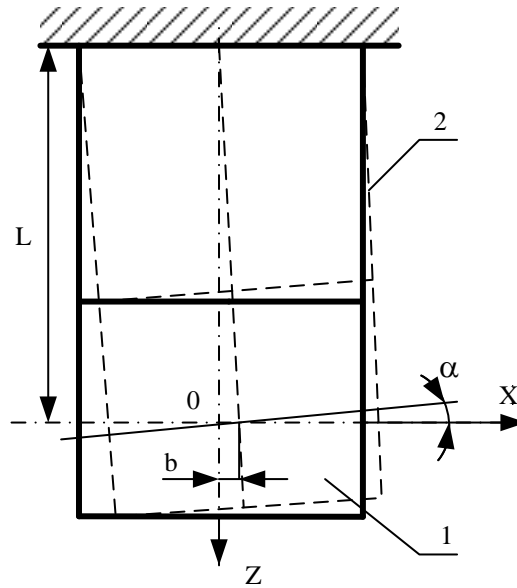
Повороты корпуса упрочнителя в процессе колебаний
